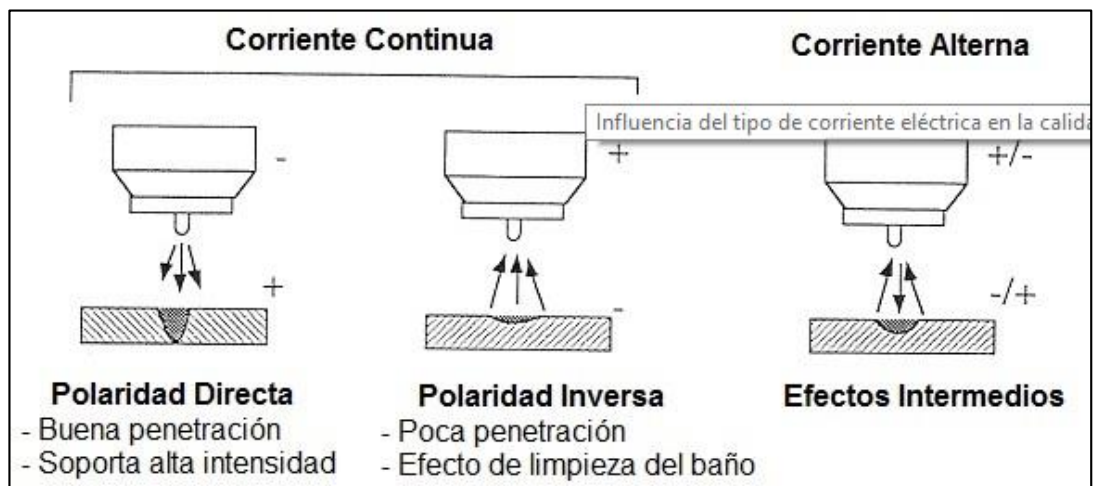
Tipos de corriente en el proceso de soldadura GTAW
